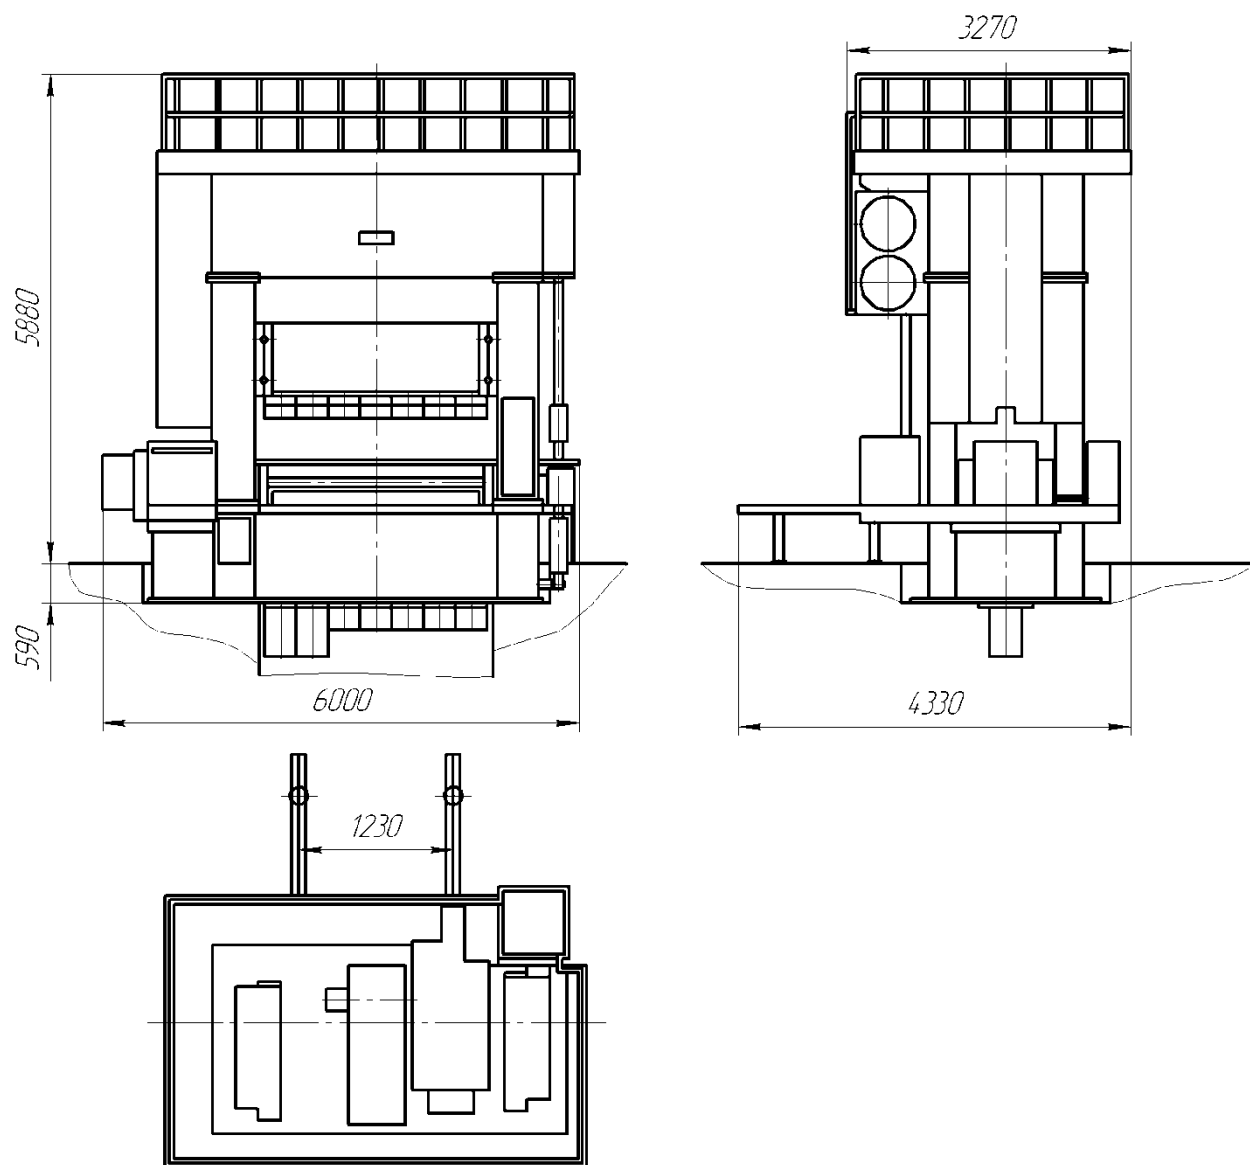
Общий вид пресса Барнаул 400 (AA6136)
